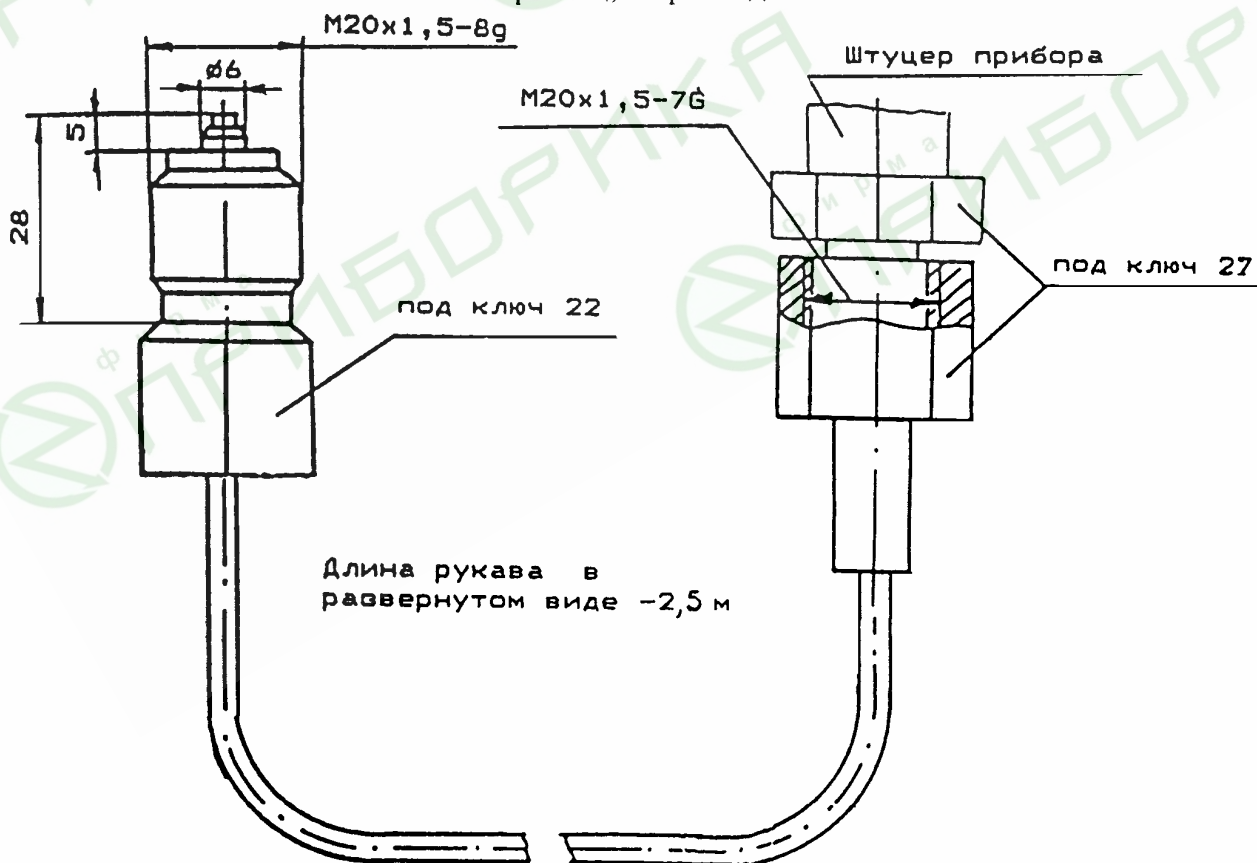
Габаритные и присоединительные размеры рукава соединительного гибкого модели 55004
